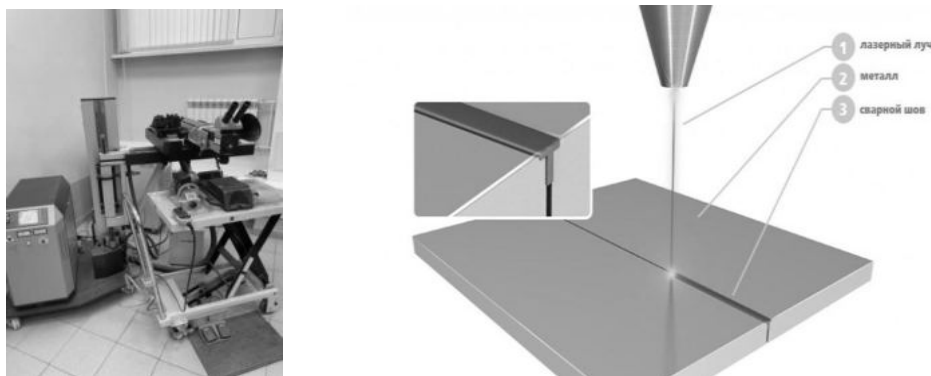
Установка импульсной лазерной сварки
